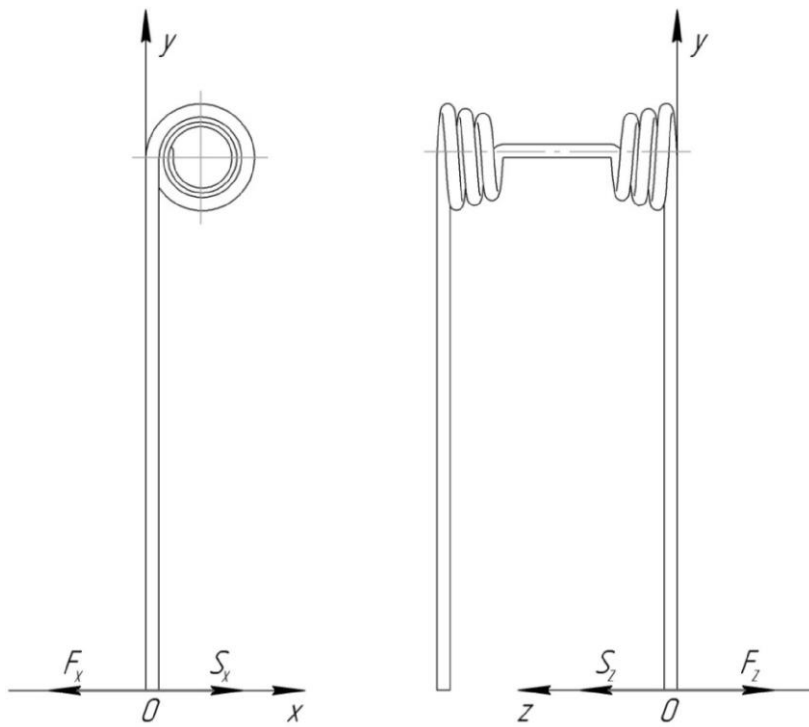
Схема сил, діючих на зубопружинний робочий орган
